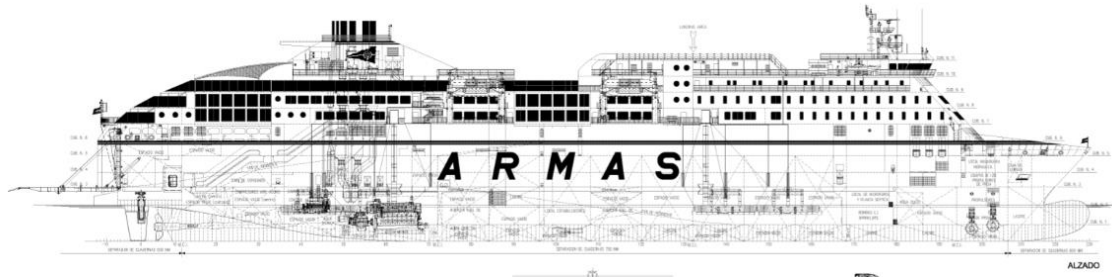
Disposición General. Fuente: Planos V. Teide
